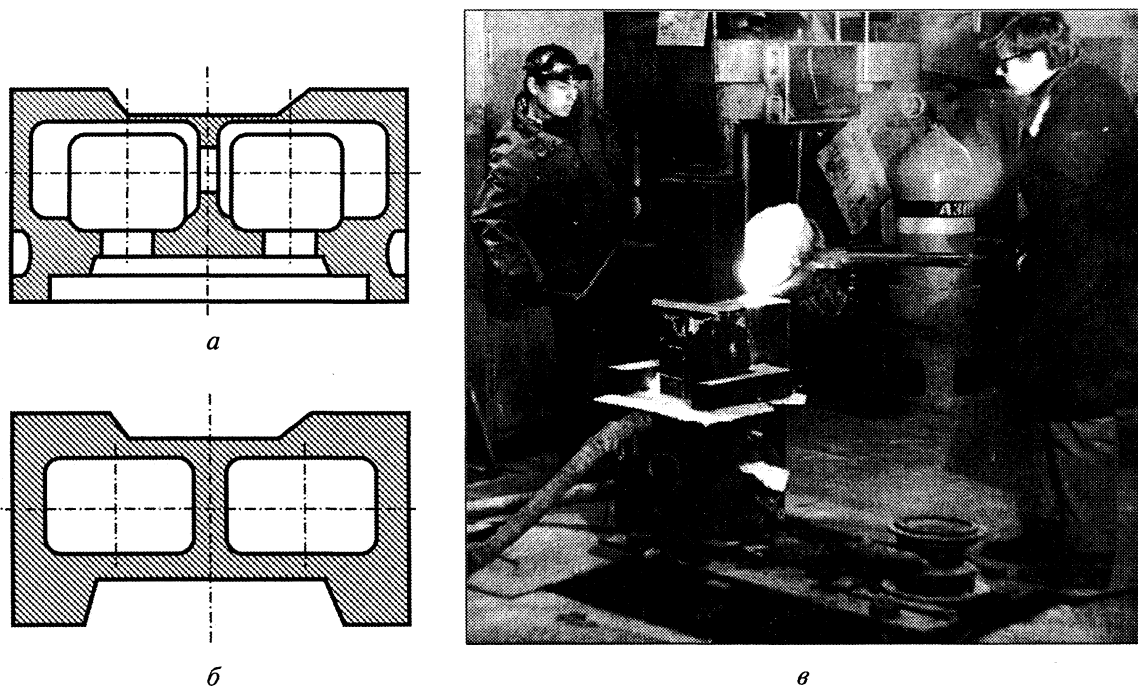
Конструкция станины балансировочного станка (*а*); измененная конструкция (*б*) и рабочий момент (*в*) заливки станины
